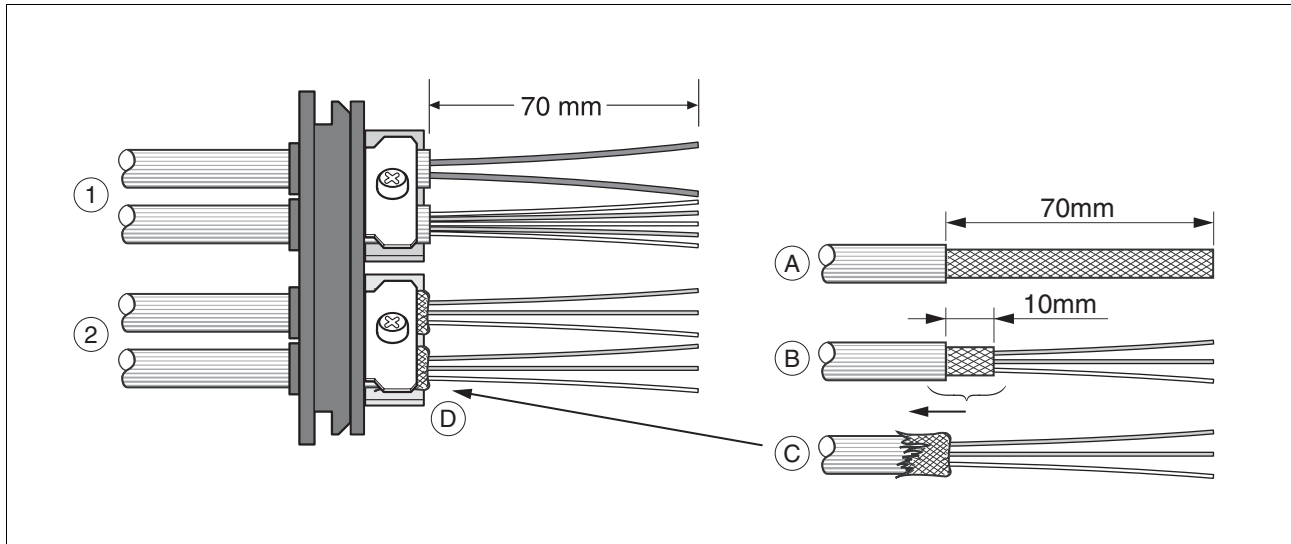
Kabel in der Kabeldurchführung befestigen
